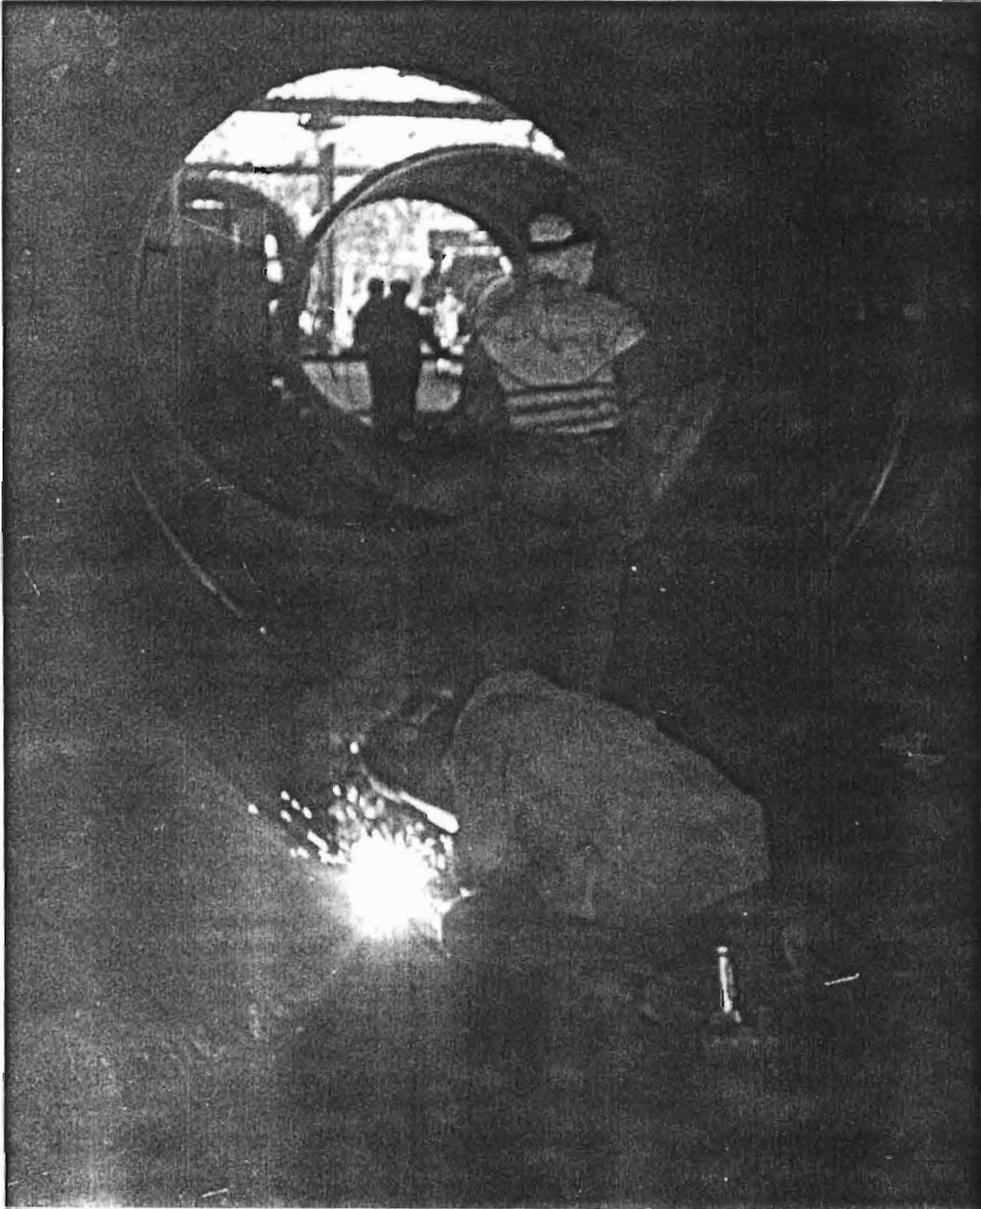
CONTROL DE REPARACION DE SOLDADURAS
